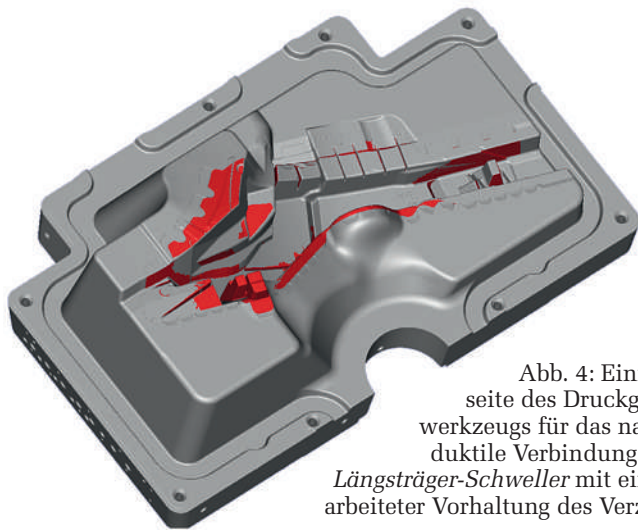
Einfüllseite des Druckgusswerkzeugs für das naturduktile Verbindungsstück Längsträger-Schweller mit eingearbeiteter Vorhaltung des Verzugs
